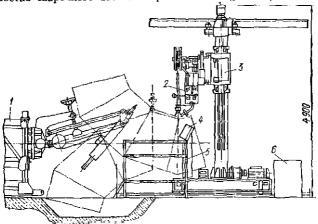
Сварочный пост при изготовлении отводов диаметром 630—1420 мм:
